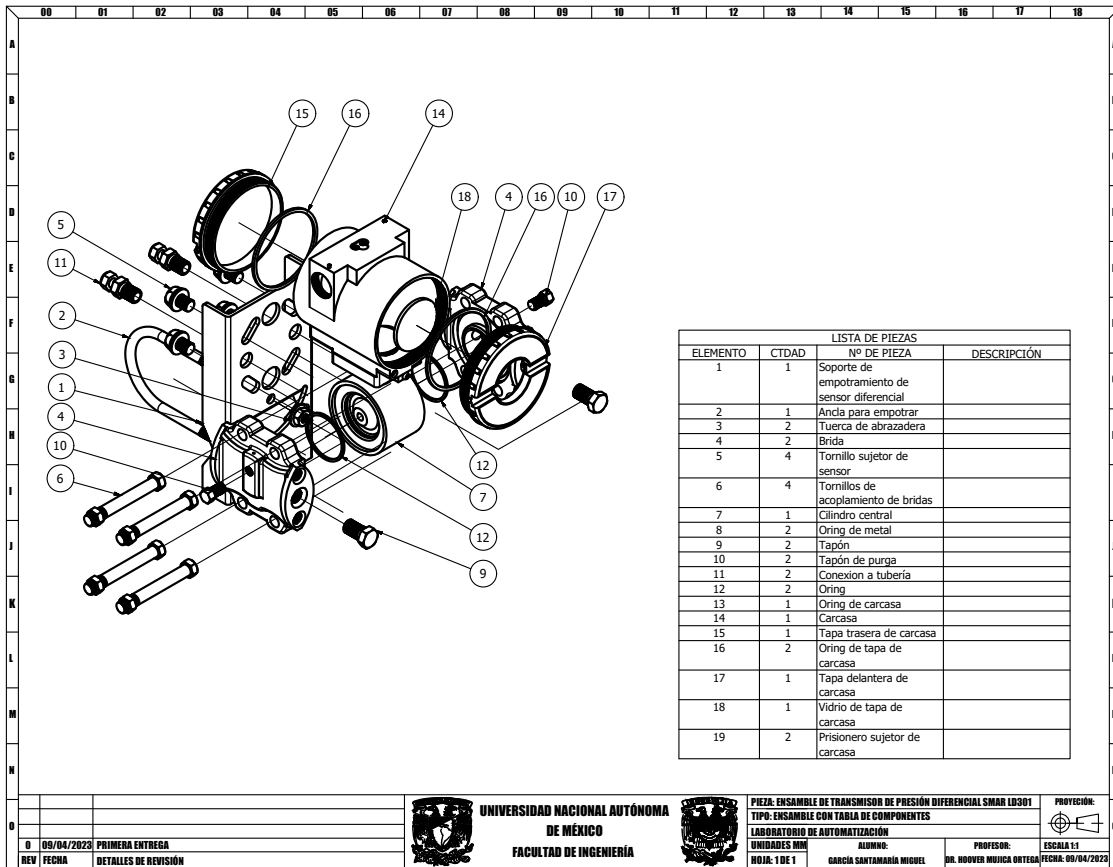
Ensamble explosionado y tabla de componentes de sensor de presión diferencial SMAR LD301
